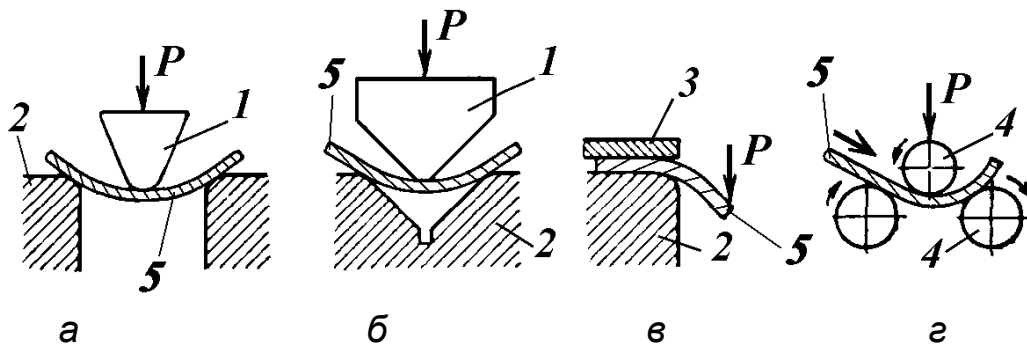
Схеми згинальних операцій: а – вільне згинання; б – згинання зі стисненням; в – консольне згинання; г – згинання прокатуванням (1 – згинальний пуансон; 2 – опора або матриця; 3 – притискач; 4 – ролики або валки; 5 – заготовка)
